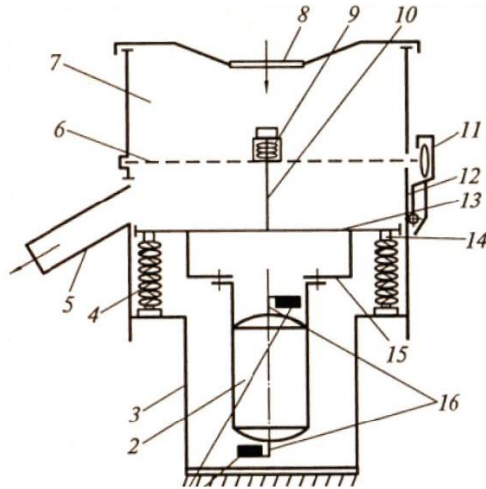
Вібраційний просіювач МВПМ – 300: 1 – дисбаланси; 2 – електродвигун; 3 – основа; 4 – пружина; 5 – розвантажувальний лоток; 6 – плоске сито; 7 – бункер; 8 – завантажувальний отвір; 9 – пружина; 10 – шпилька; 11 – клямка; 12 – корпус; 13 – днище; 14 – штир; 15 – кронштейн; 16 – робочий вал
